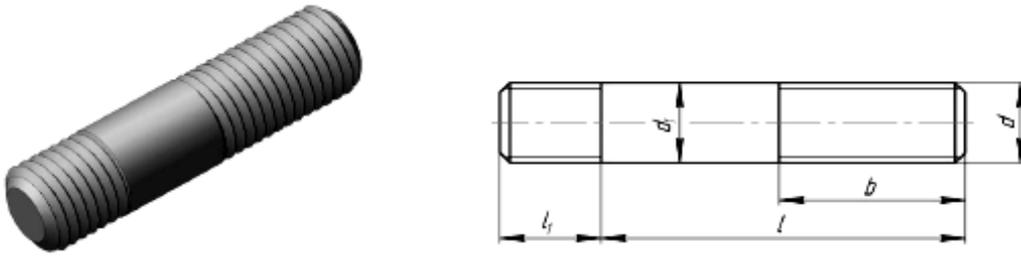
Шпилька общего назначения исполнения 1
